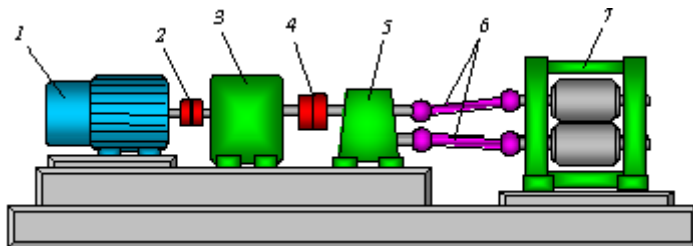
Одноклетьевого прокатный стан: 1 – электродвигатель; 2 – муфта моторная; 3 – редуктор; 4 – муфта коренная; 5 – шестеренная клетка; 6 – шпиндель; 7 – рабочая клетка
